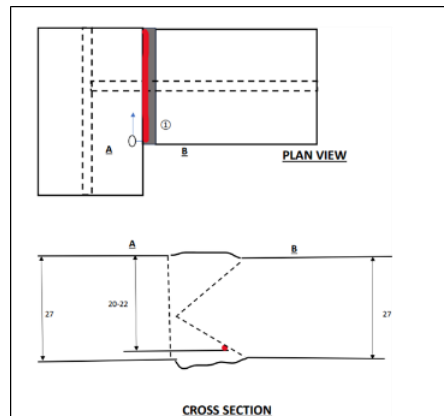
3 Contoh Cacat ESI (Excessive Spatter Inclusion)
